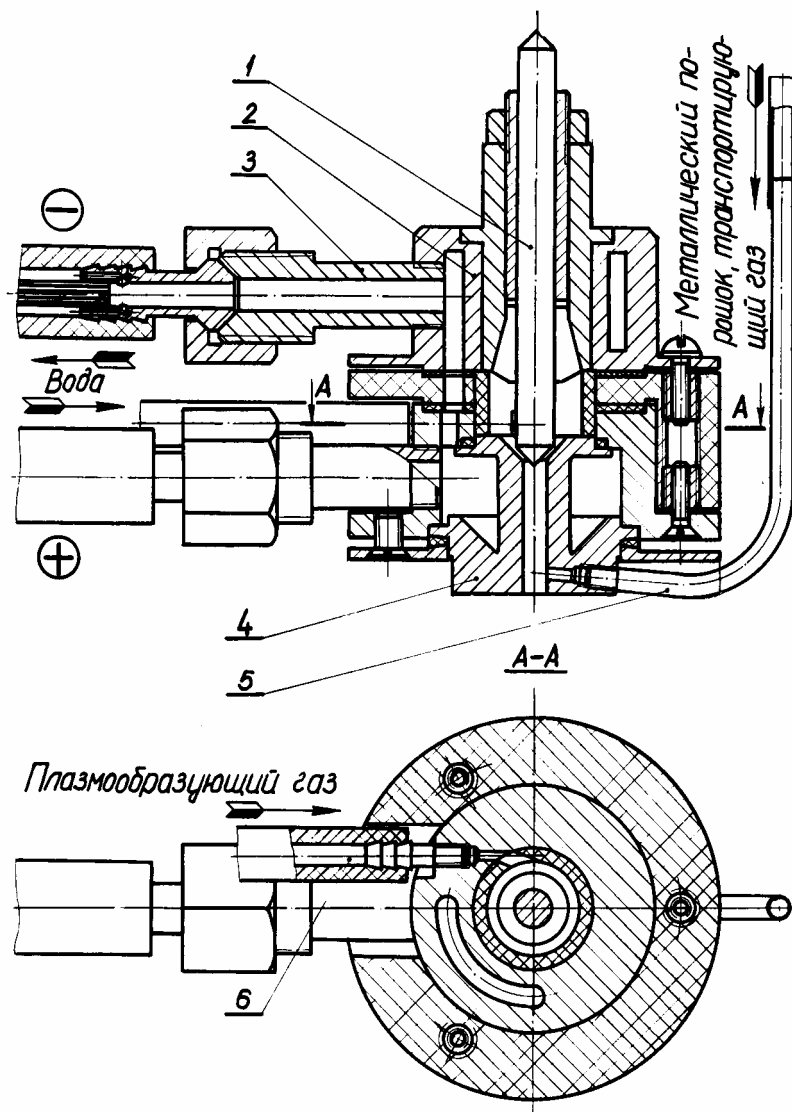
Плазменная горелка для напыления порошкового материала: 1 – электрод-катод; 2 – корпус; 3 – подвод охлаждающей воды; 4 – сопло-анод; 5 – подвод порошка; 6 – подвод плазмообразующего газа
